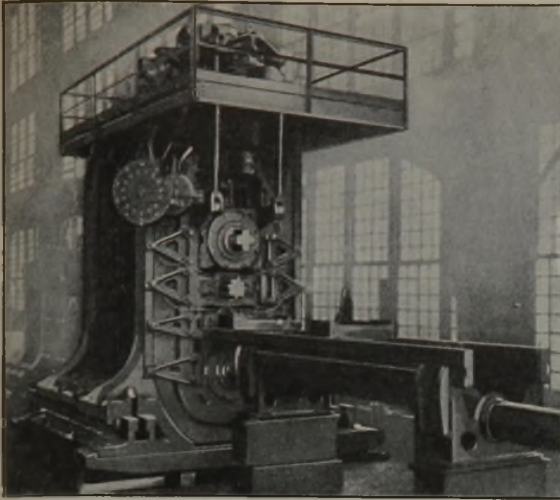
Fertiggerüst mit Walzenausbauvorrichtung.
